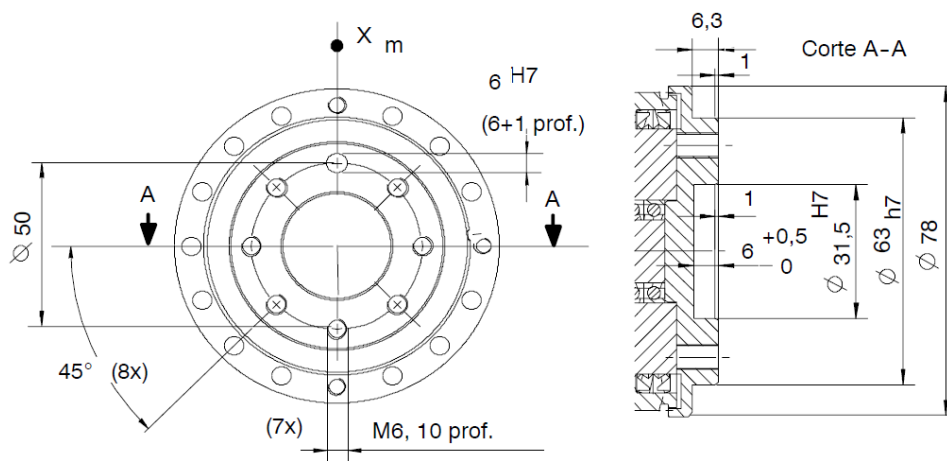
Dimensiones brida de montaje del brazo robot KUKA KR 16
